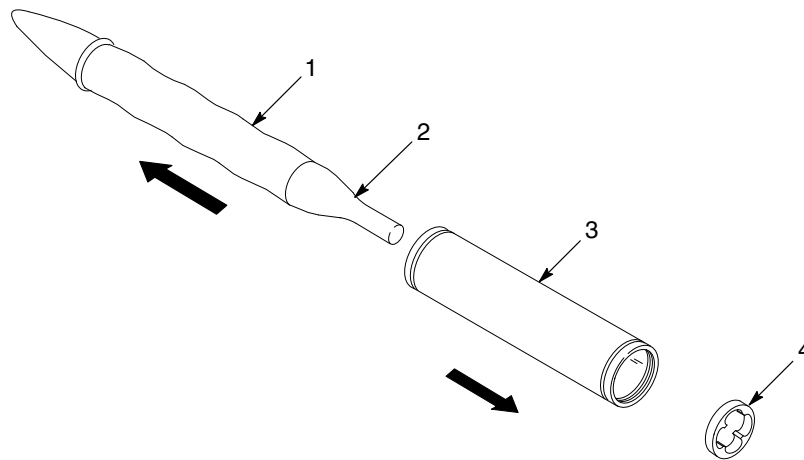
Instalar o módulo de carga – passos 3 e 4
